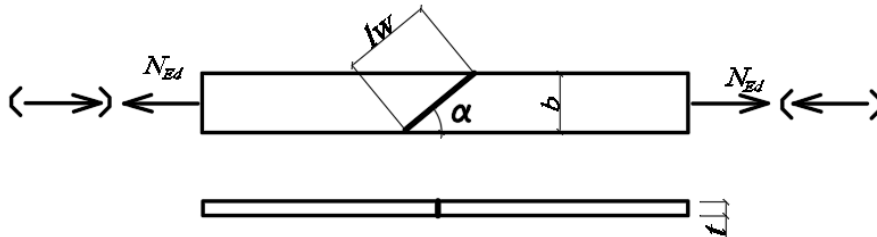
Косой стыковой сварной шов
